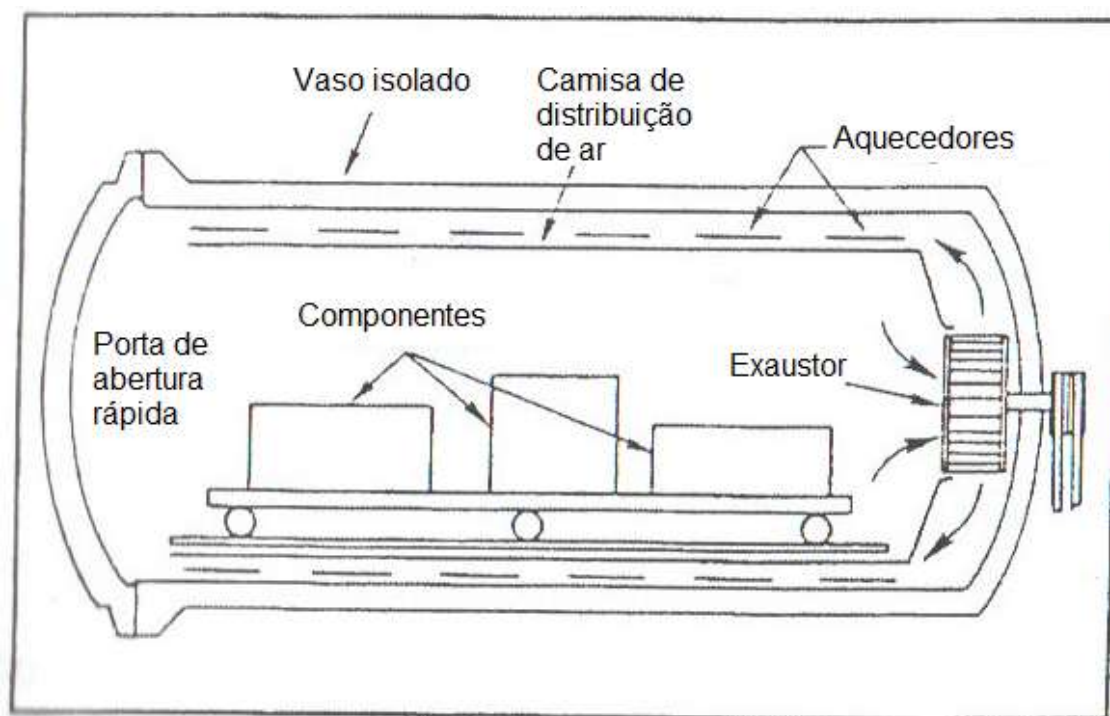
Desenho esquemático do processo de moldagem utilizando autoclave.
